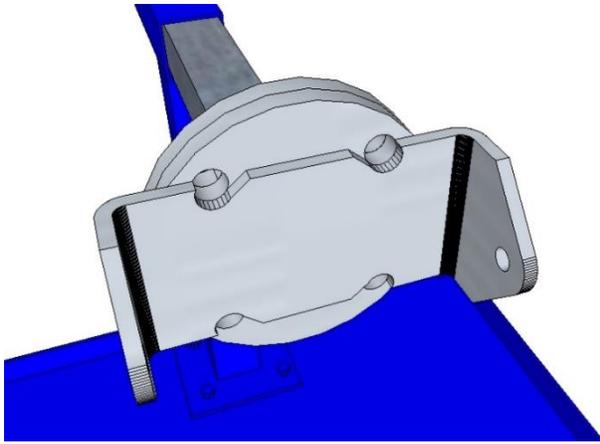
Disco soldado en horquilla de fijación en 3D.
